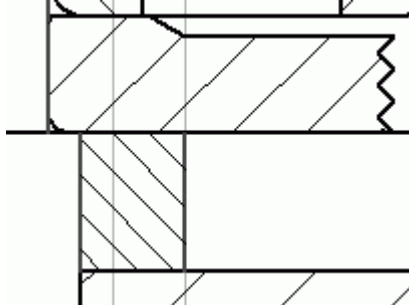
Распорное кольцо для осевой фиксации зубчатого колеса
